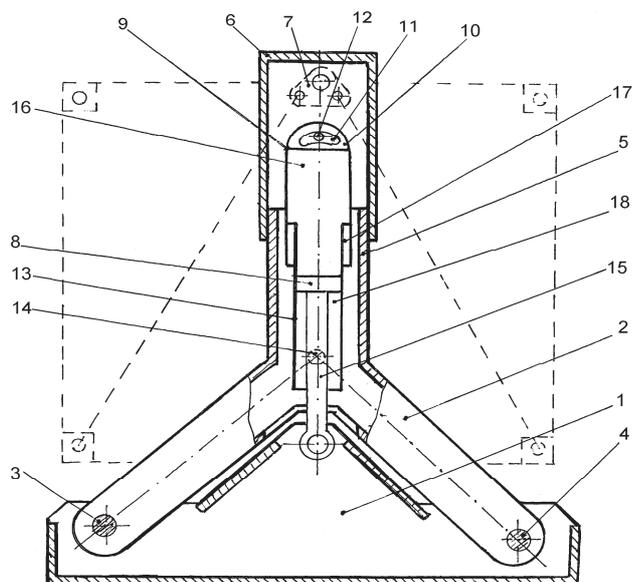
Грузоподъемный механизм контейнеровоза-перегружателя
